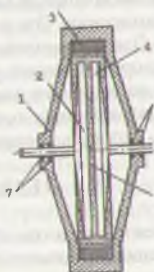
Порошковая муфта: 1-корпус; 2,4-стальные диски; 3-катушка; 5-контакты; 6-ферромагнитная масса.
